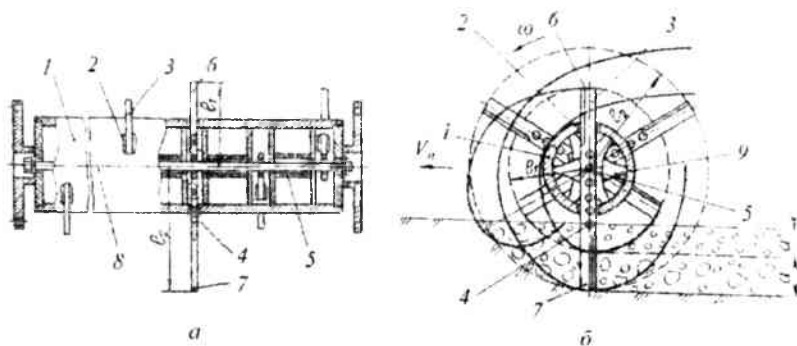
Универсальный ротационный рабочий орган: 1 – трубчатый вал; 2 – отверстия для установки ножей; 3 – ножи; 4 – регулировочные отверстия ножей; 5 – фиксирующий элемент; 6 и 7 – противоположные вершины ножей; 8 – ось вращения ротора; 9 – опорные кронштейны
